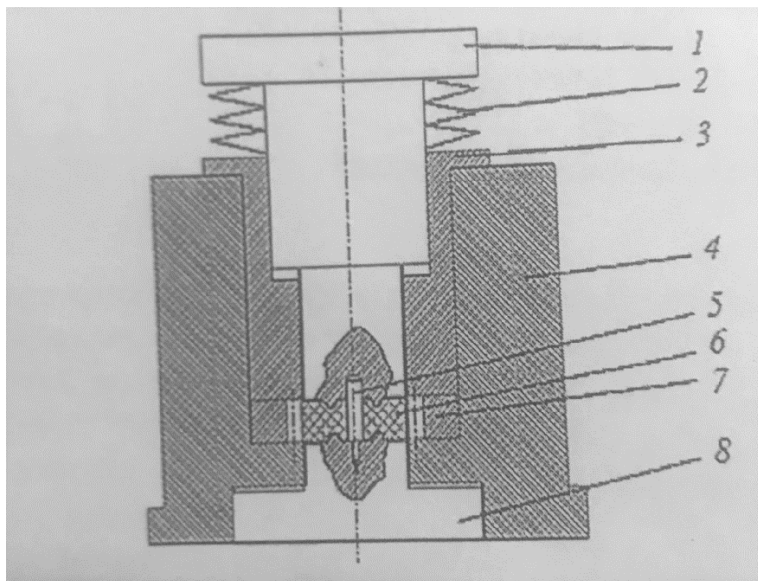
Пресс-форма для штамповки зубчатых колёс из композиционных термопластов
